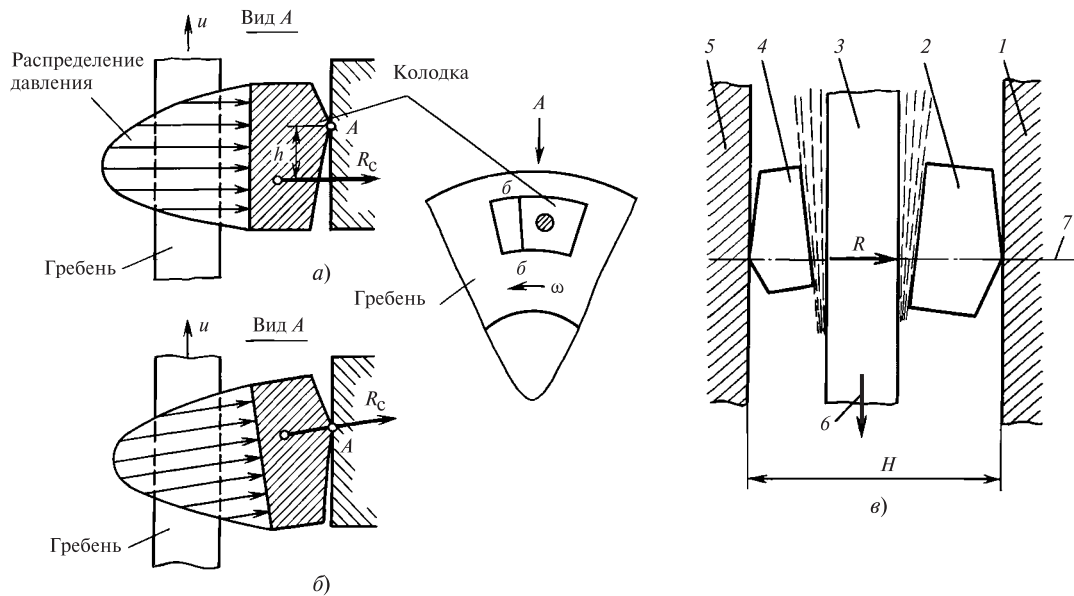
Положения гребня упорного подшипника между упорными колодками:
